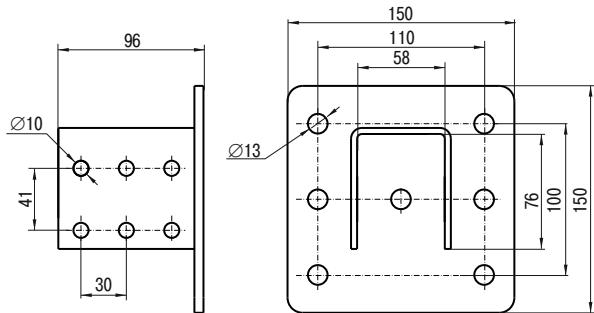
Крепление потолочное двойное для П-образного профиля / Figure 3. Double ceiling mounting fitting for U-shaped profile
